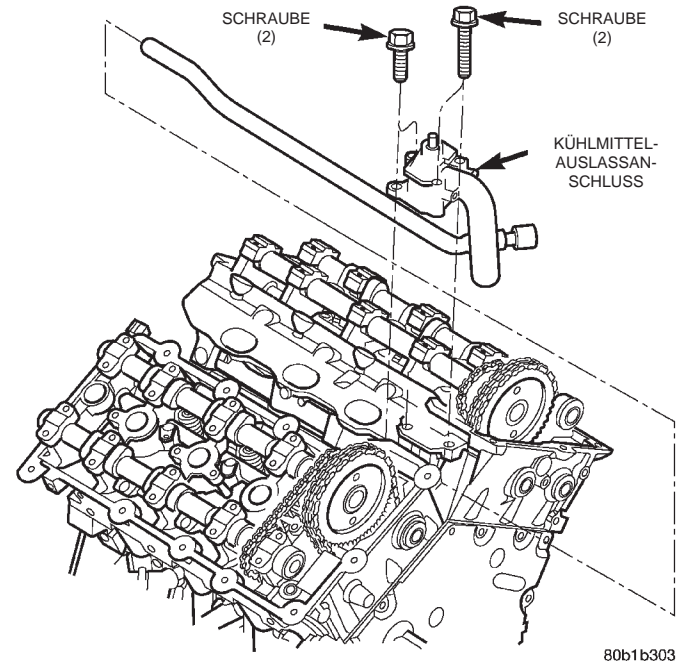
Kühlmittel-Auslaßanschluß—Aus- und Einbau
